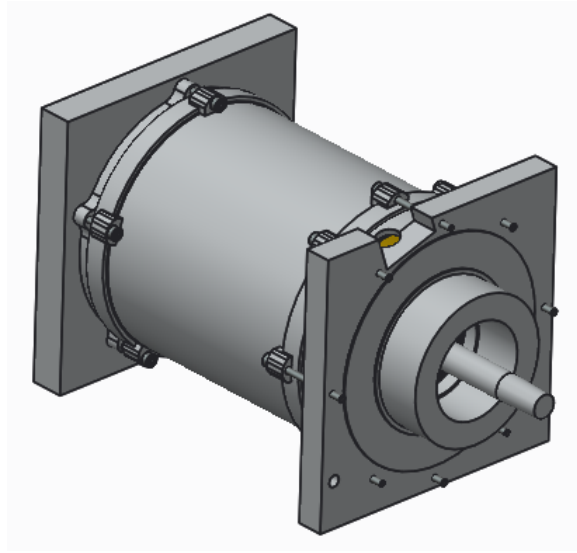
Vue d’ensemble du modèle par ordinateur du moteur prototype
